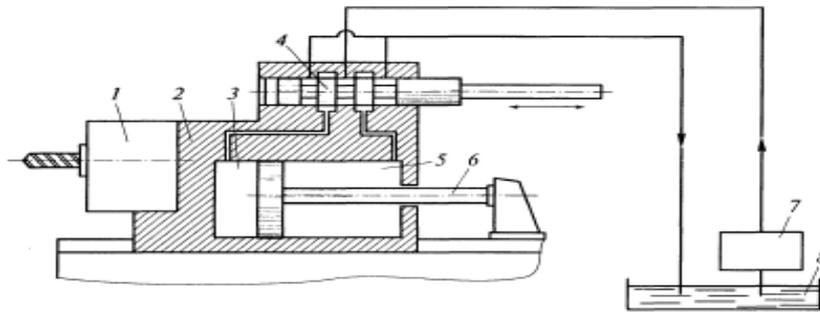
Схема гидравлической следящей системы поступательного движения: 1— механизм, несущий режущий инструмент; 2 — гидроцилиндр; 3 — левая часть гидроцилиндра; 4 — золотник; 5 — правая часть гидроцилиндра; 6 — шток поршня; 7— насос; 8 — резервуар.
